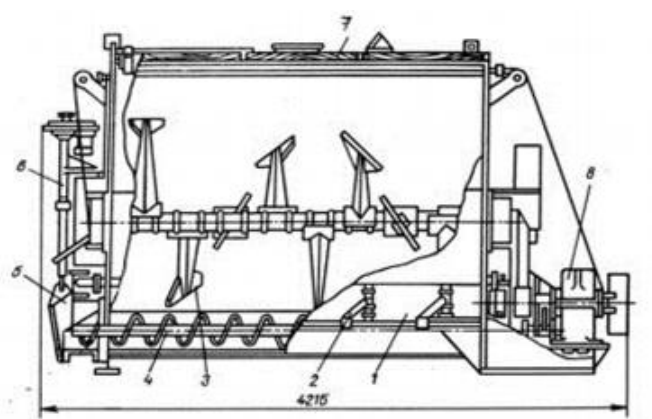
Схема змішувача С-12: 1 – корпус; 2 – паророзподільник; 3 – лопатевий змішувач; 4 – вивантажувальний шнек; 5 – вивантажувальний патрубок із клиновою засувкою; 6 – система керування; 7 – кришка; 8 – привід [1].
